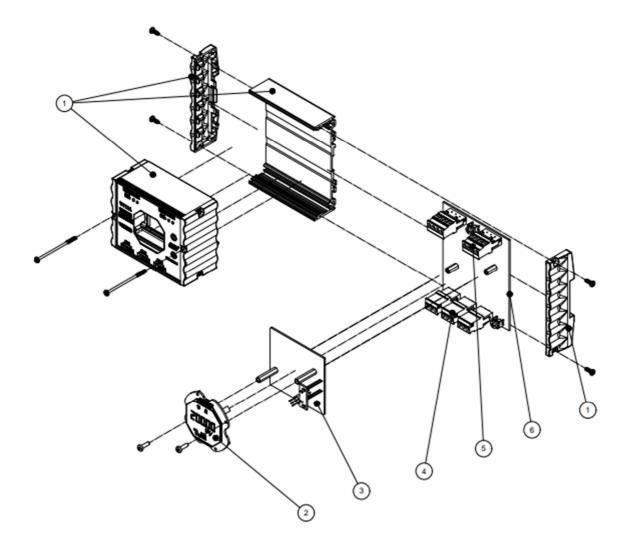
Desenho dimensional e esquema de montagem do VTT11-PP.
